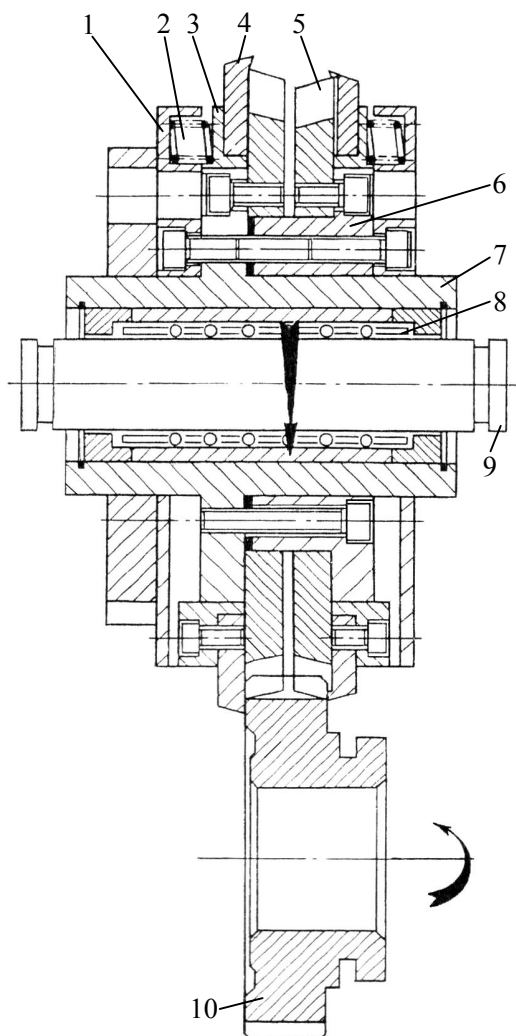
Конструкция инструментального блока для одновременного образования фасок и снятия заусениц с двух сторон зубчатого колеса: 1 – кронштейн; 2 – пружина; 3 – прижим; 4 – дисковые резцы; 5 – фасочные инструментальные зубчатые колеса; 6 – кронштейн; 7 – корпус приспособления; 8 – подшипниковый плавающий узел; 9 – ось; 10 – обрабатываемое зубчатое колесо
